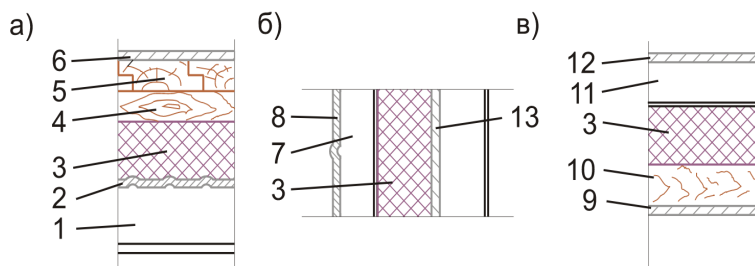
Устройство теплоизоляции изотермического вагона: а) — пола; б) — стены; в) — крыши; 1 — поперечная балка вагона; 2 — металлический гофрированный лист; 3 — теплоизоляция; 4 — деревянная поперечная балка; 5 — верхний настил пола; 6 — оцинкованный лист; 7 — вертикальная стойка стены; 8 — наружная стальная обшивка; 9 — обшивка потолка; 10 — деревянная потолочная дуга; 11 — стальная потолочная дуга; 12 — стальная обшивка крыши; 13 — стальная внутренняя обшивка с вертикальными гофра
